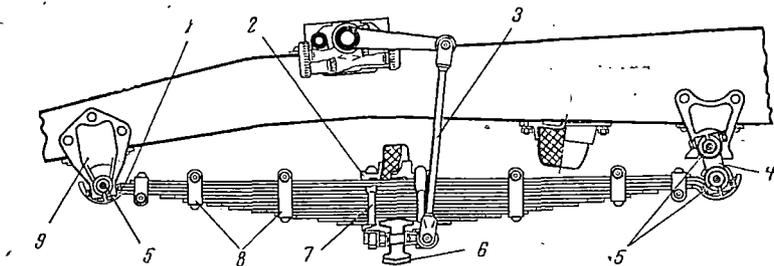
Передняя рессора автомобиля ГАЗ-51А:
